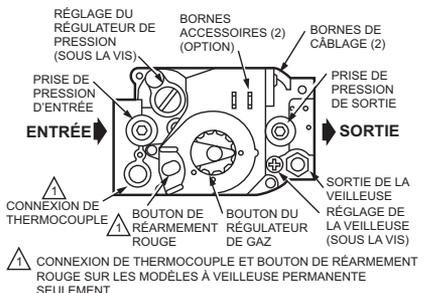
Vue de haut des régulateurs à gaz combinés VR82xx, VR83xx, A, H, K et M.
